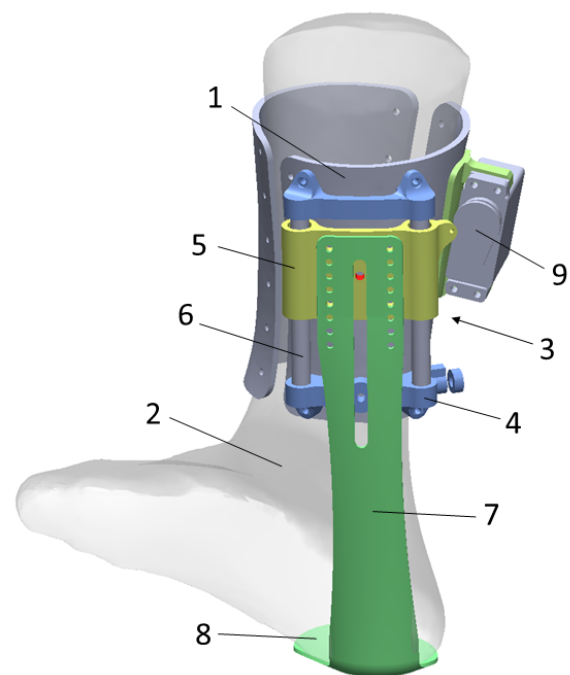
Diseño CAD de la órtesis planteada para absorción de la carga axial durante el apoyo del pie.
